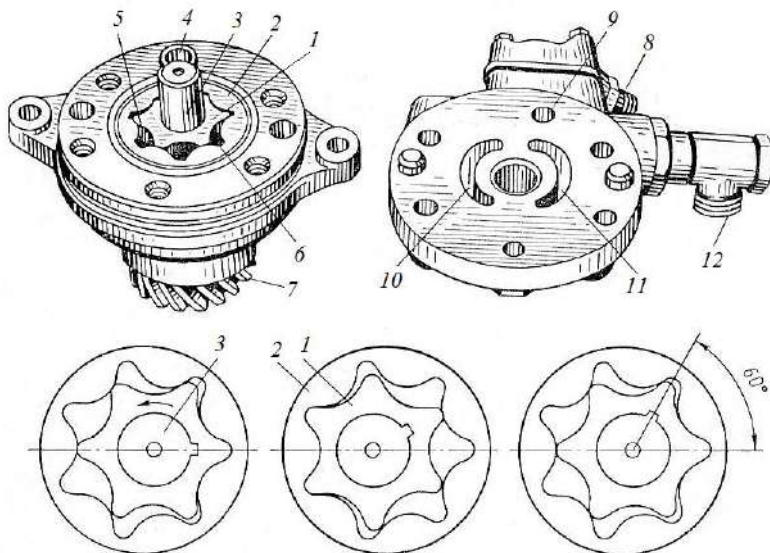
Шестеренний гідралічний насос з внутрішнім зачепленням та схема його дії:
